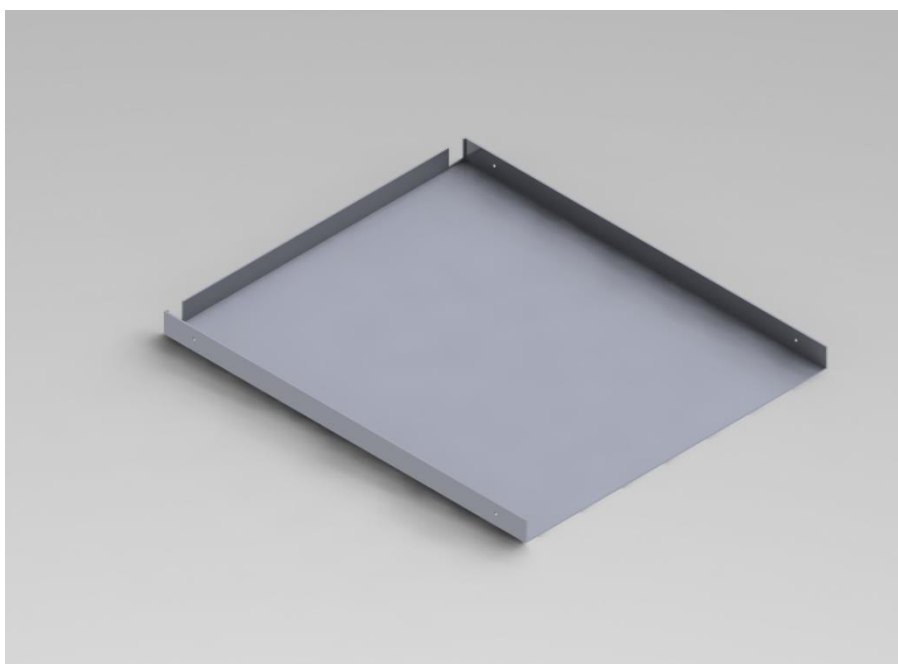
Ensamble subconjunto 1.3. Soldadura 1.
